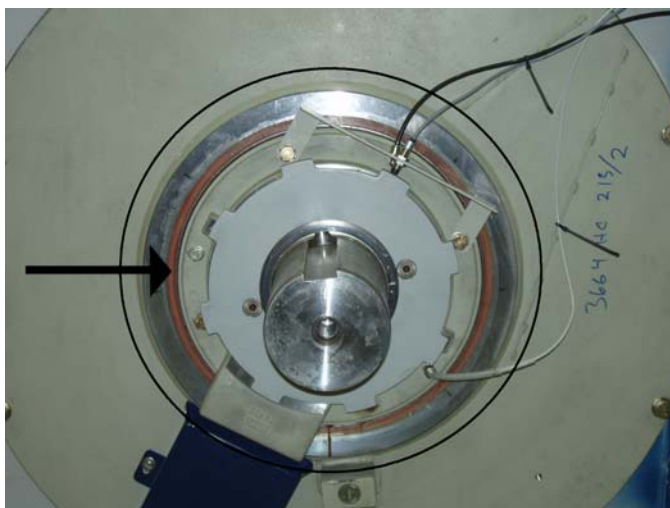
Изоляция подшипника и поверхность концевого щитка
